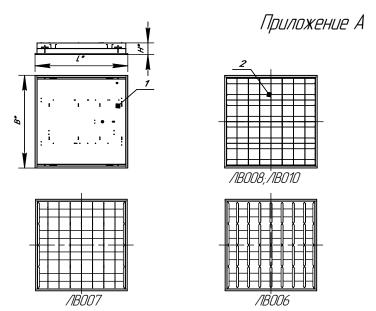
;2;3: 1. Корпус в сборе, 2. Решётка в сборе.
